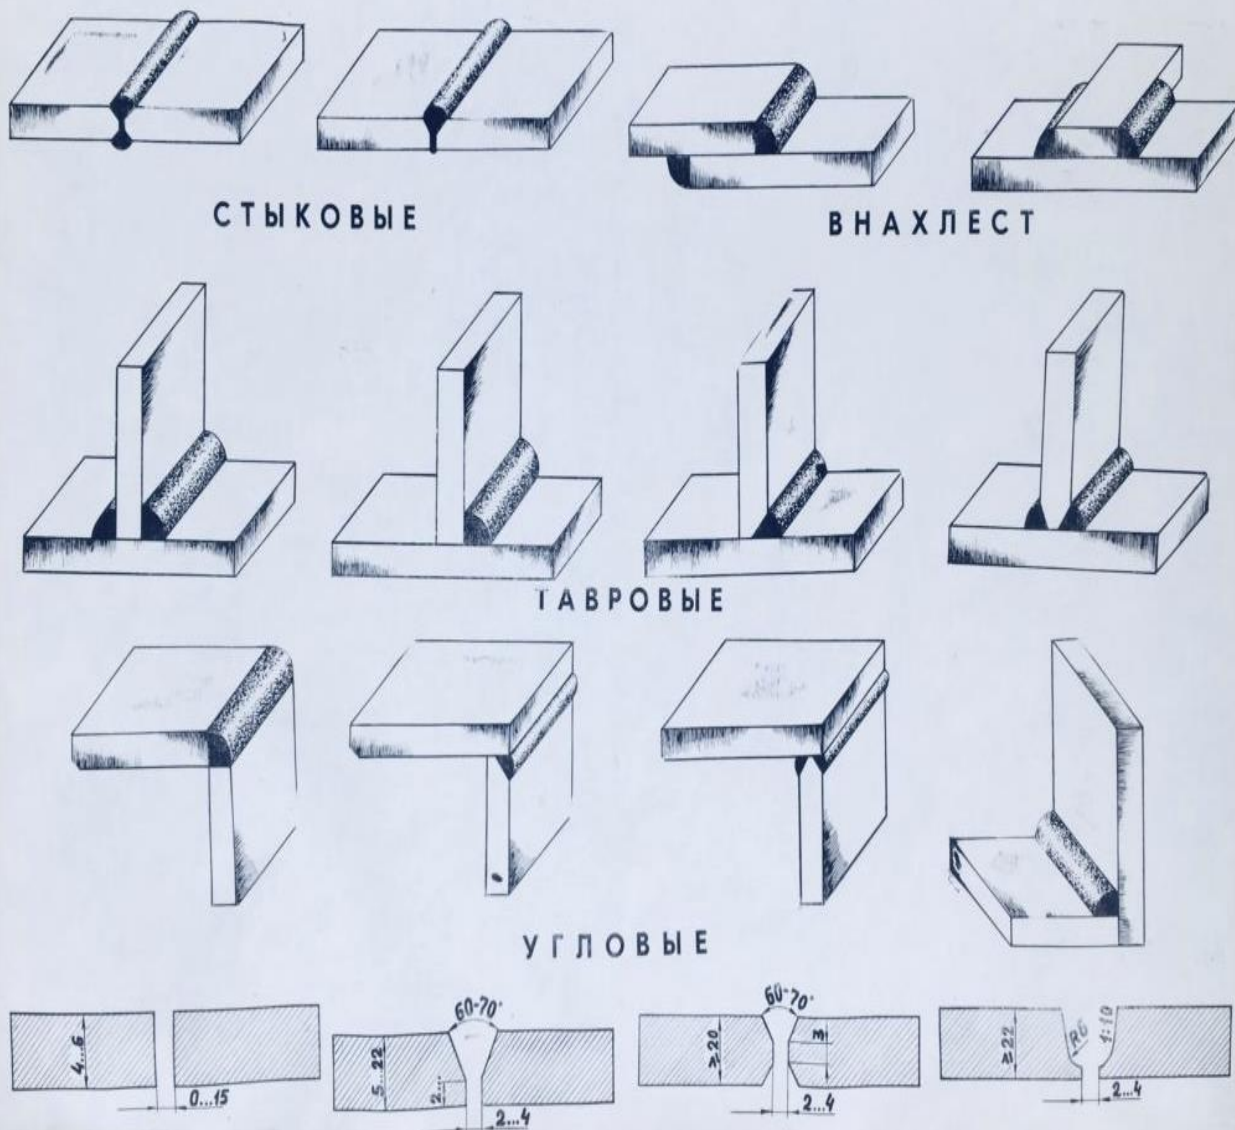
Виды сварных соединений пластмасс
